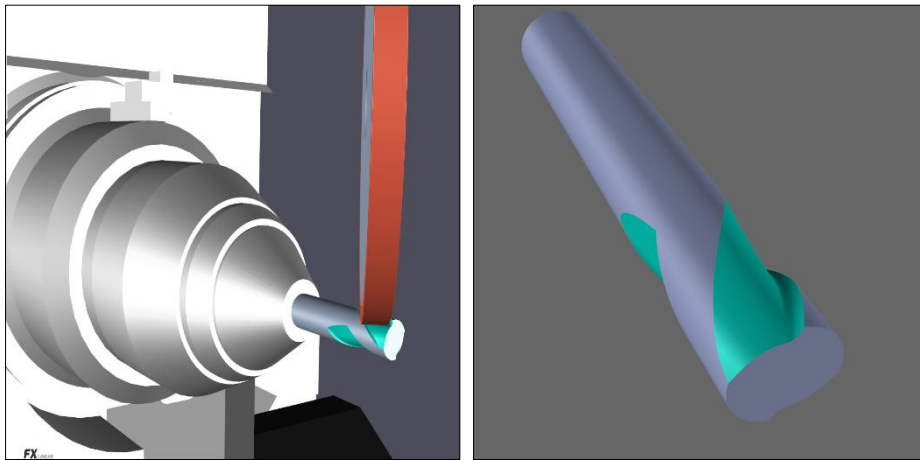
Ø12 Ballnose end mill taş paketi
